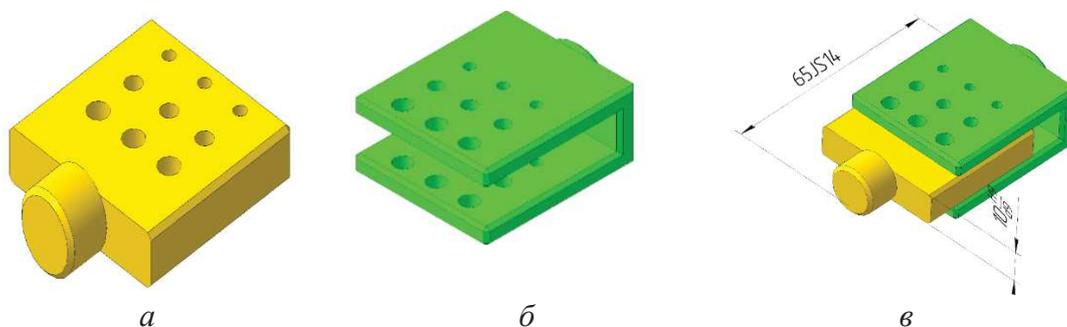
Общий вид приспособления для проведения испытаний заклепочных соединений
